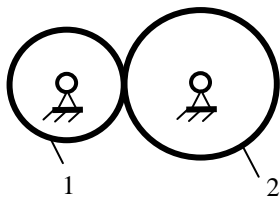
Зубчатая передача с внешним зацеплением колёс
